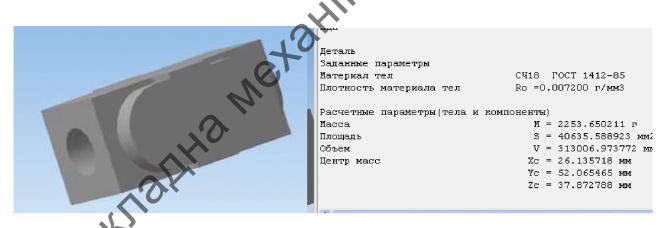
Визначення маси заготовки для лиття в піщано-глинисті форми з машинним формуванням
